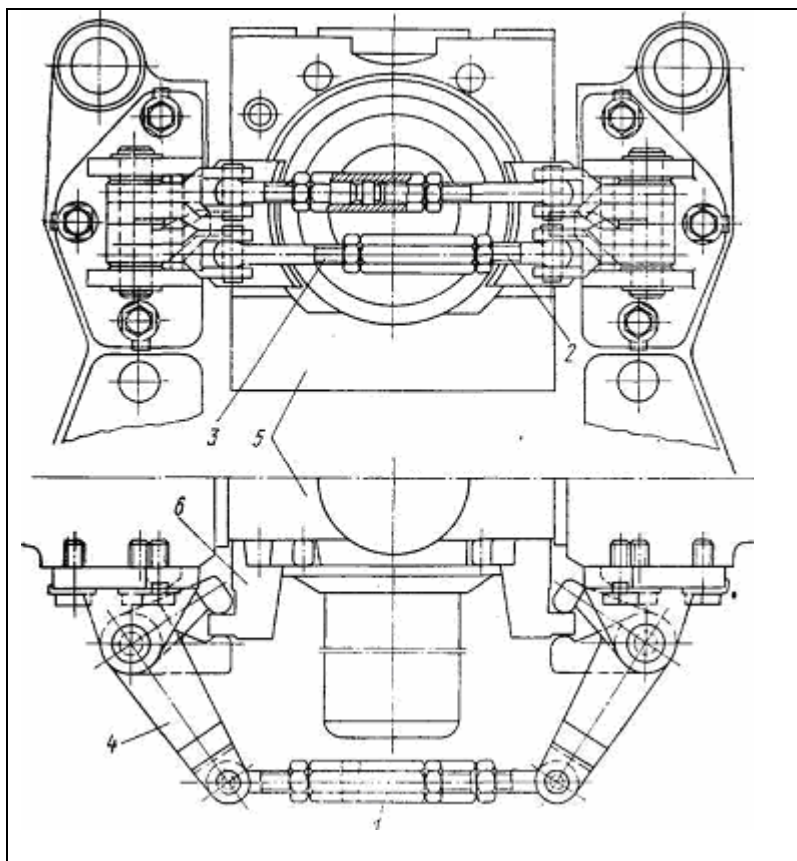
Устройство для осевой регулировки валков: 1 – гайка; 2,3 – тяга; 4 – рычаг; 5 - подушка
